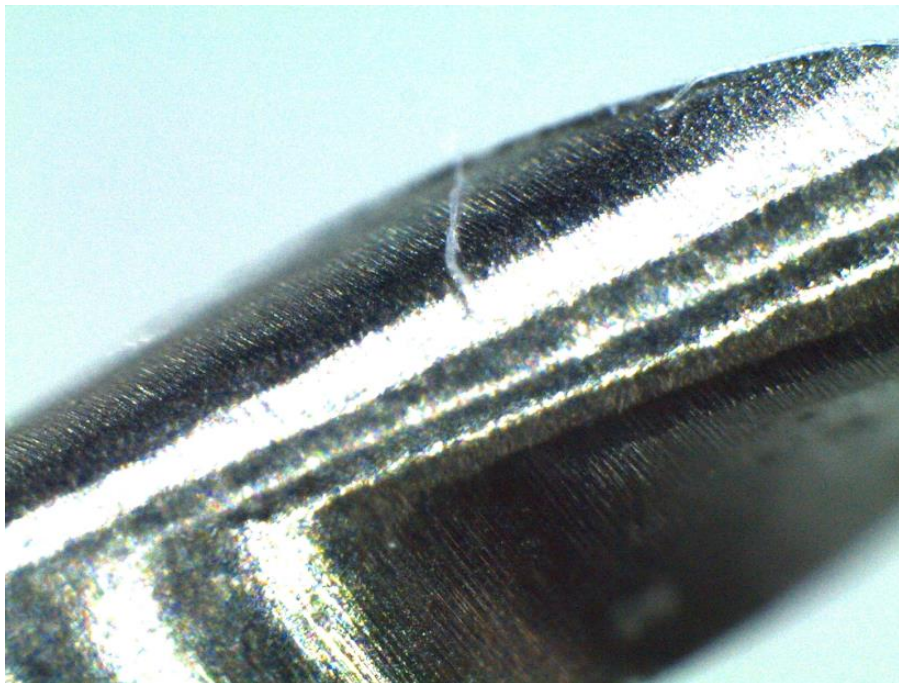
Crack o defecto de fábrica. Instrumento fue excluido
